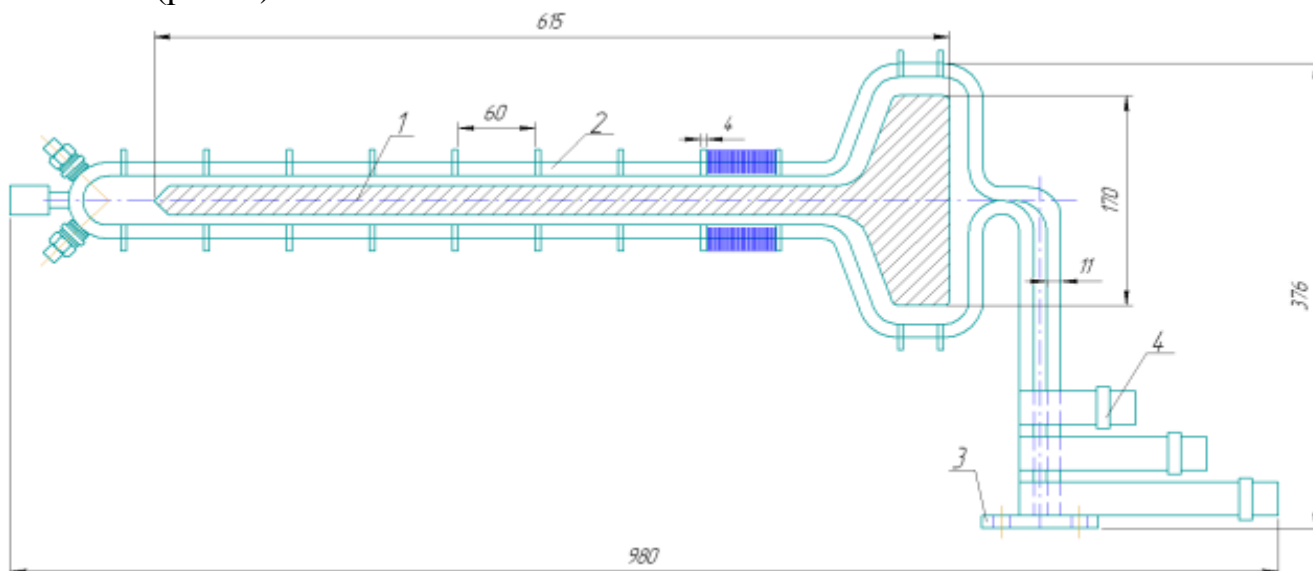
Эскиз индуктора для закалки шпангоутов: 1 – сечение шпангоута; 2 – магнитопровод; 3 – щека крепления к закалочному трансформатору; 4 – штуцер охлаждения
